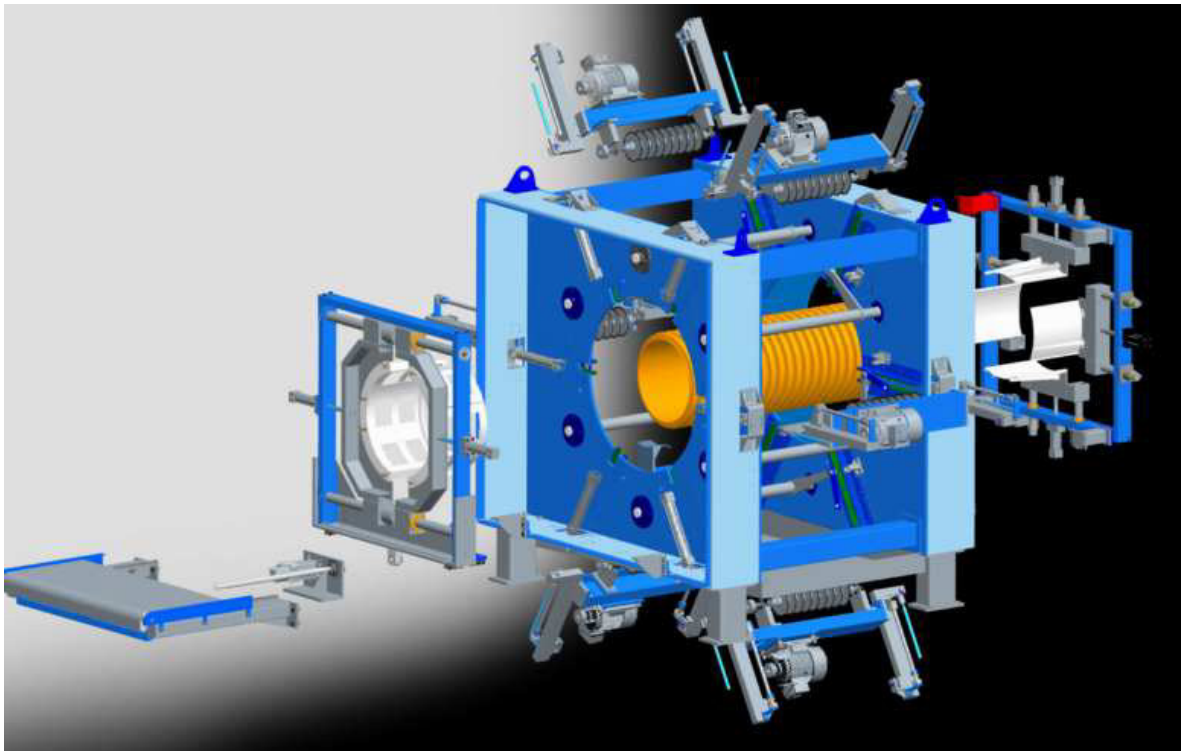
Serra de Dreno - Vista explodida (Periplast 2014)
